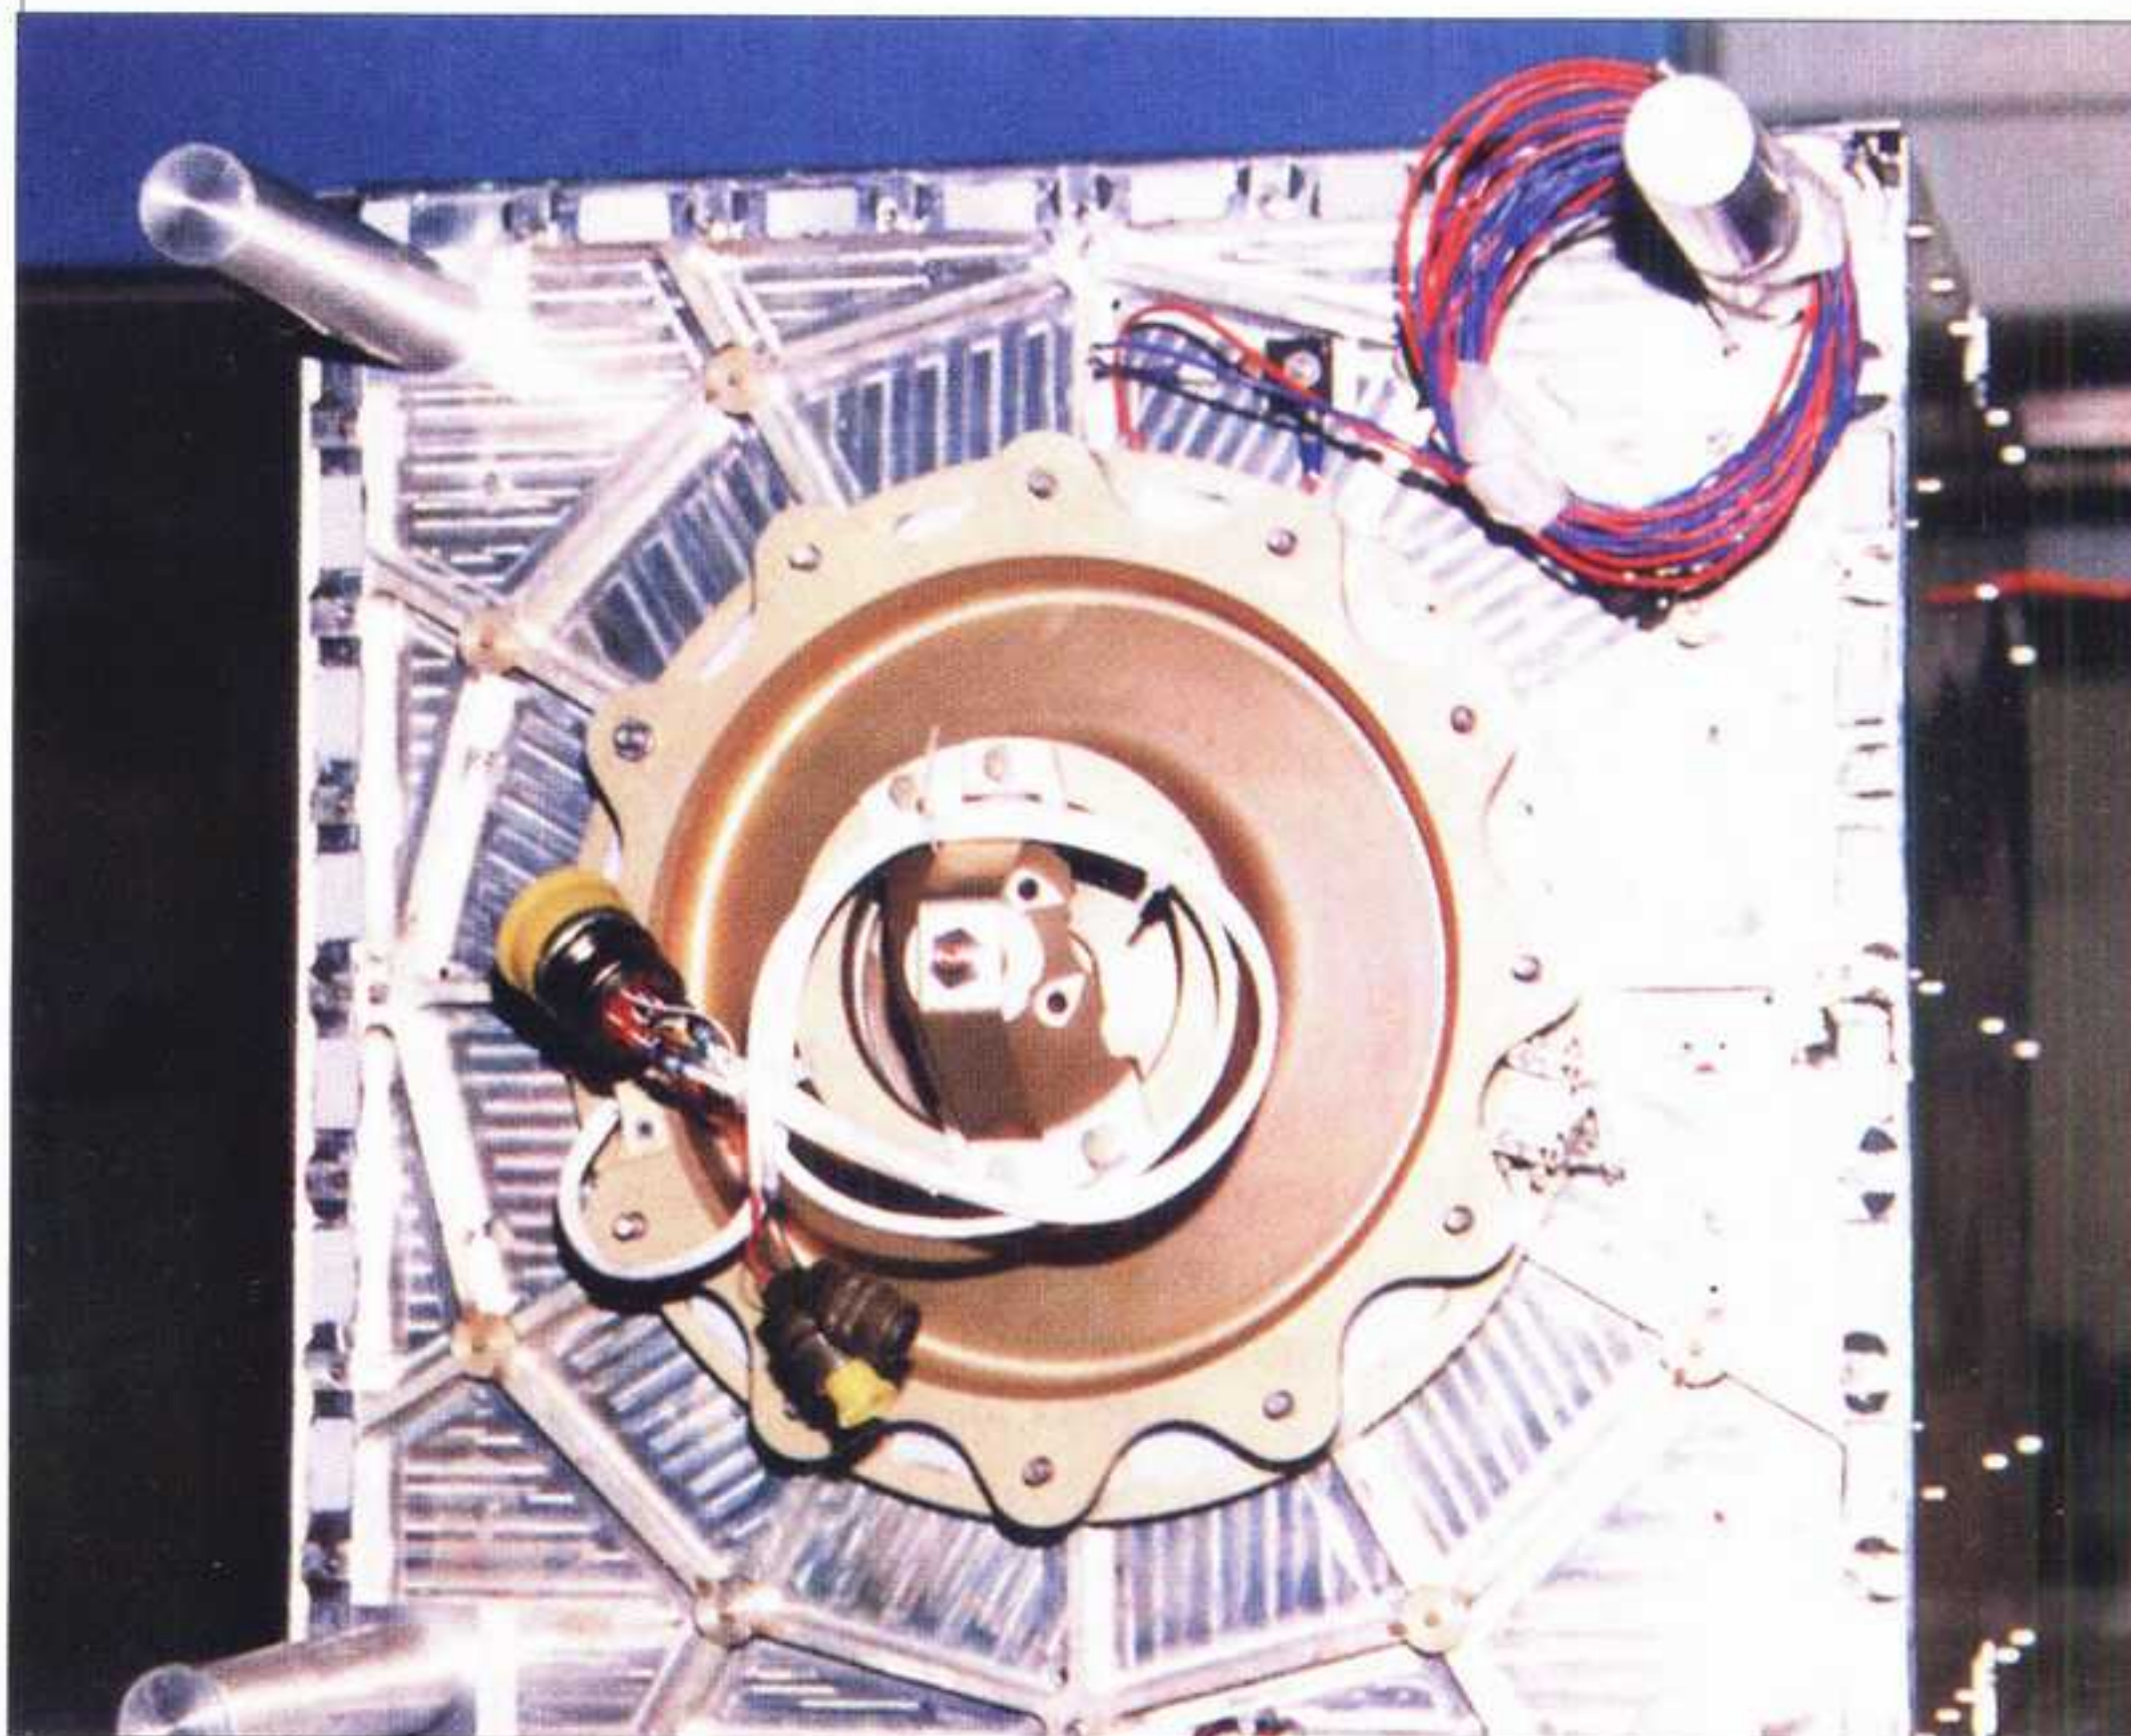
Vista de la bandeja inferior del UPM-Sat 1 con el sistema de separación para carga secundarias instaladas en la plataforma ASAP de Ariane 4-40. En esta fotografía la cara exterior de la bandeja todavía no está recubierta por la manta aislante multicapa correspondiente por lo que se pueden apreciar los detalles del mecanizado de la bandeja. (Foto: Escuela Técnica Superior de Ingenieros Aeronáuticos.)
